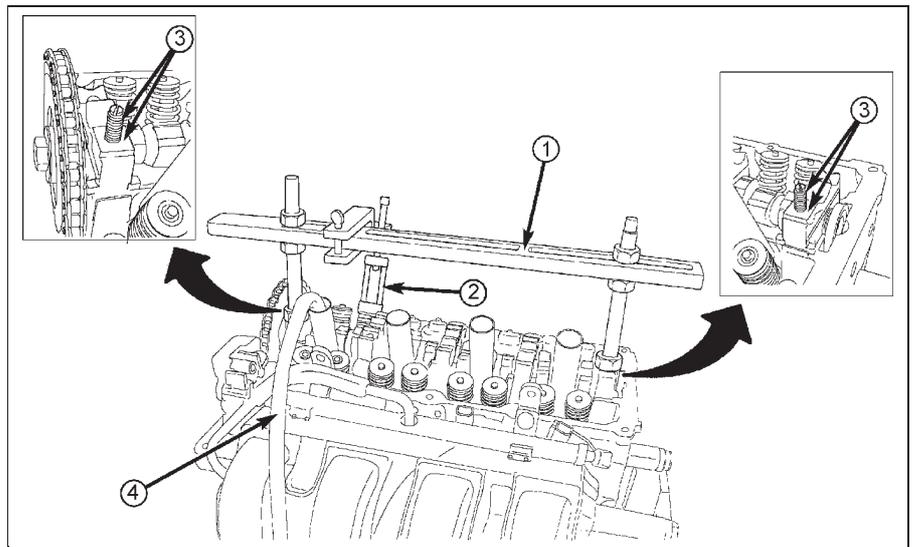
Клапанная пружина и маслоъемный колпачок - обслуживание на автомобиле - пример. 1 - рейка приспособления для сжатия пружин, 2 - приспособления для сжатия пружин, 3 - проставки, 4 - шланг подачи сжатого воздуха.
